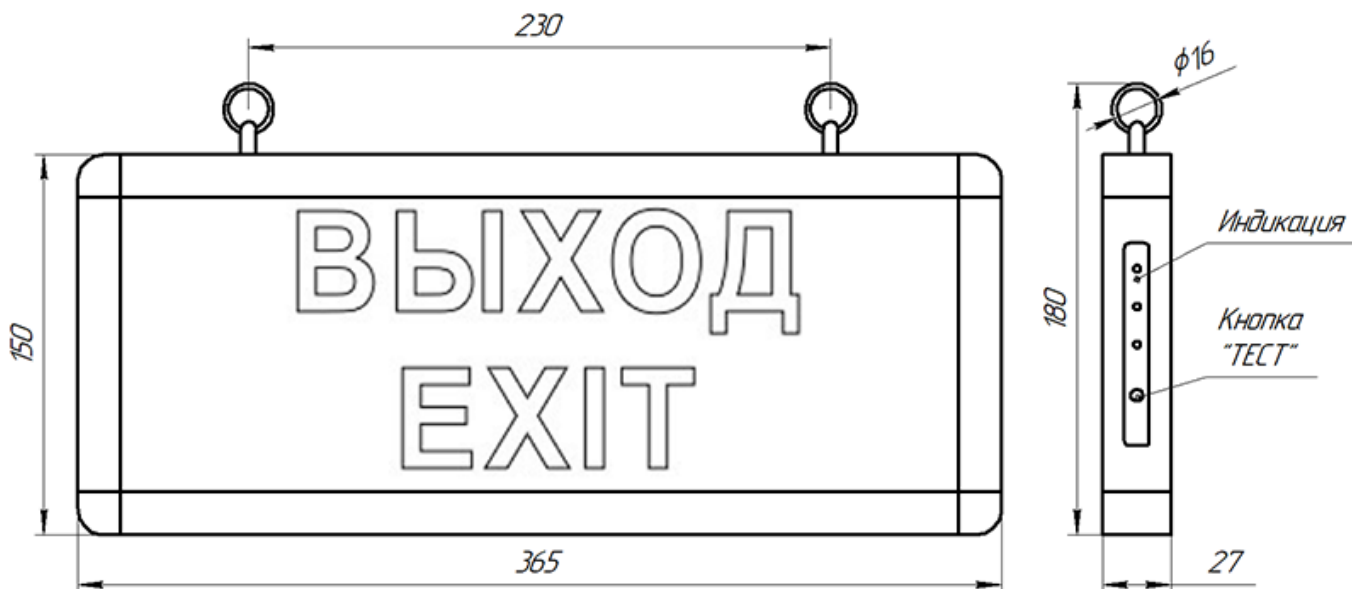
Габаритный чертёж светового указателя серии Vegas
